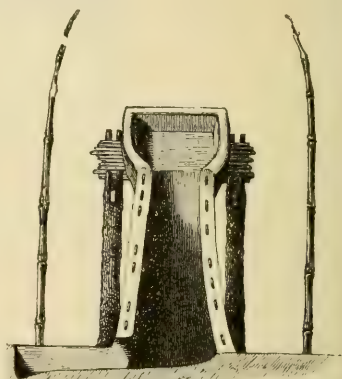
Coupe verticale suivant la ligne a b du plan.
